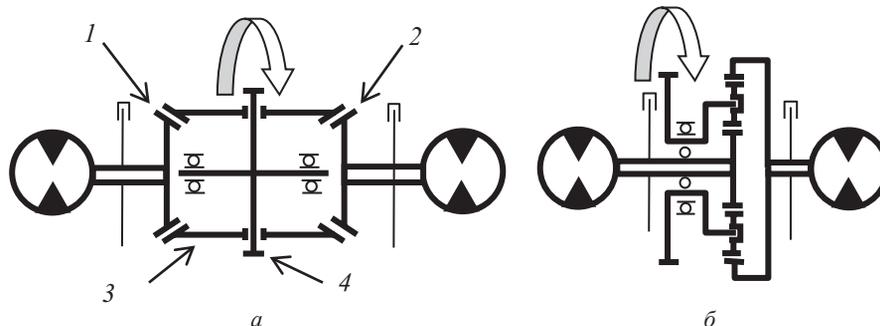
Схемы механического дифференциального блока ОГП–ЧУ с коническими (а) и цилиндрическими (б) зубчатыми колесами
